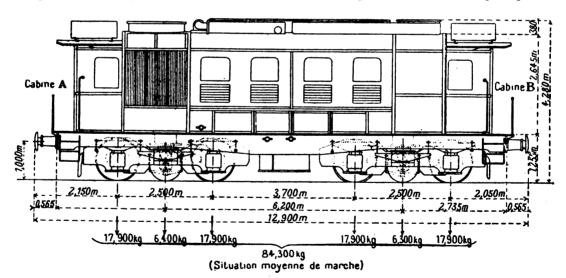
Schema della locomotiva Diesel-elettrica.
